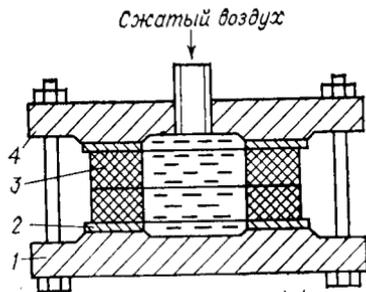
Приспособление для пропитки углеграфитовых колец:
